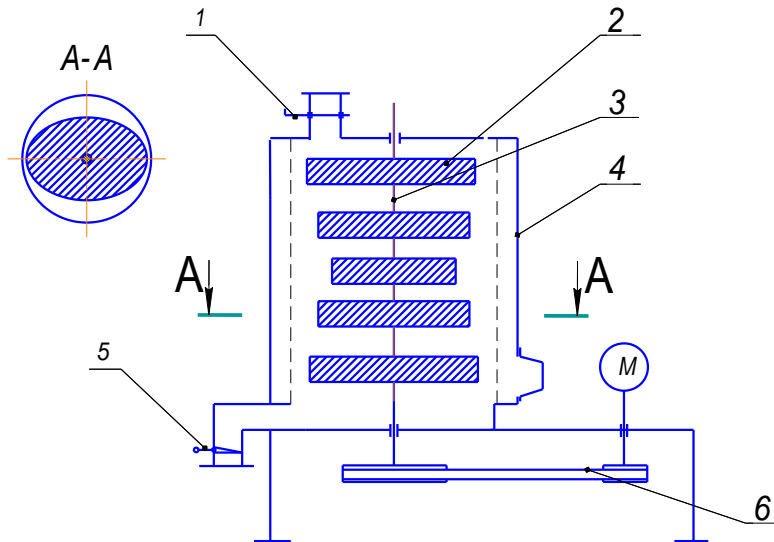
Машина роторно-дискова: 1,5-регулятор; 2-диск; 3-вал; 4-корпус; 6-привід.
